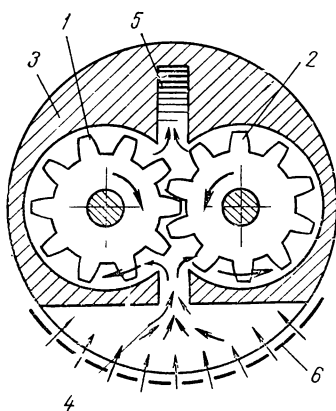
Шестеренчатый насос: 1, 2 — шестерни; 3 — корпус насоса; 4 — всасывающее отверстие; 5 — нагнетающее отверстие; 6 — сетка-фильтр
